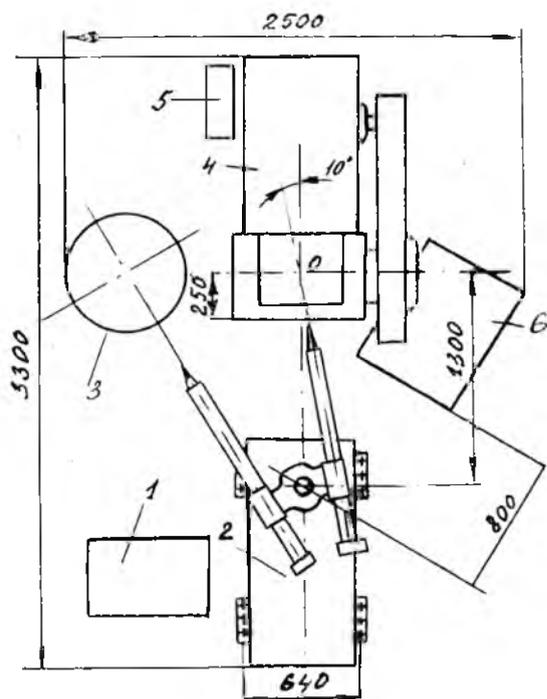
РТК холодной штамповки деталей массой до 2 кг на прессе, обслуживаемом ПР
